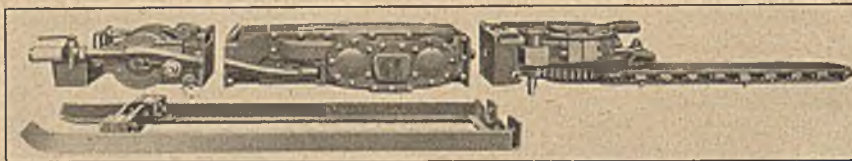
Zusammenbau der Maschine für Druckluftantrieb und Schrämkette.
